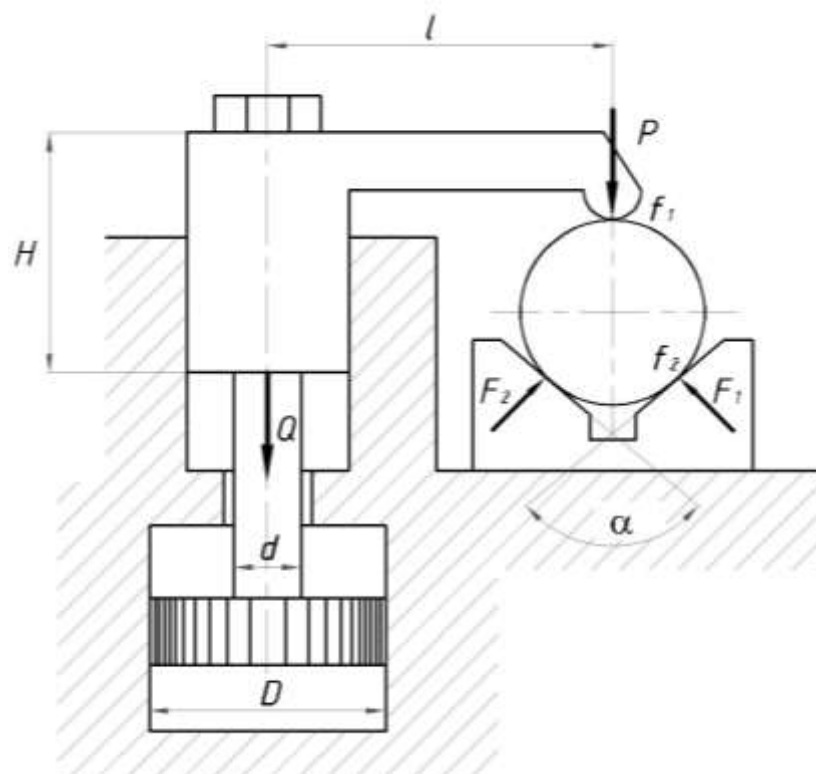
Схема базування та затиску деталі в пристрої для фрезеруванні пазів
